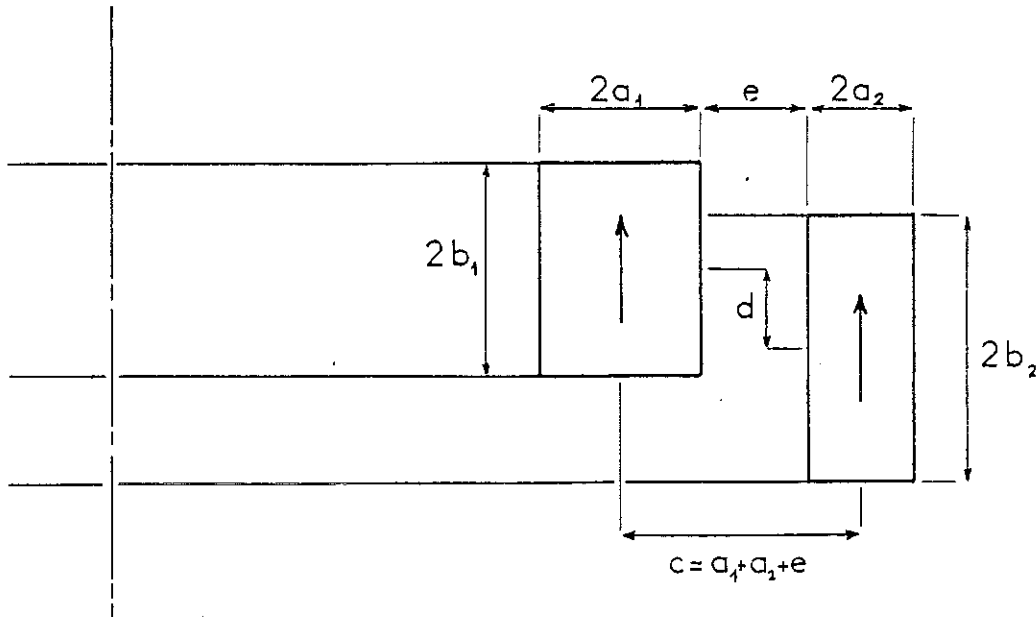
Palier magnétique de type A : Définition des dimensions
